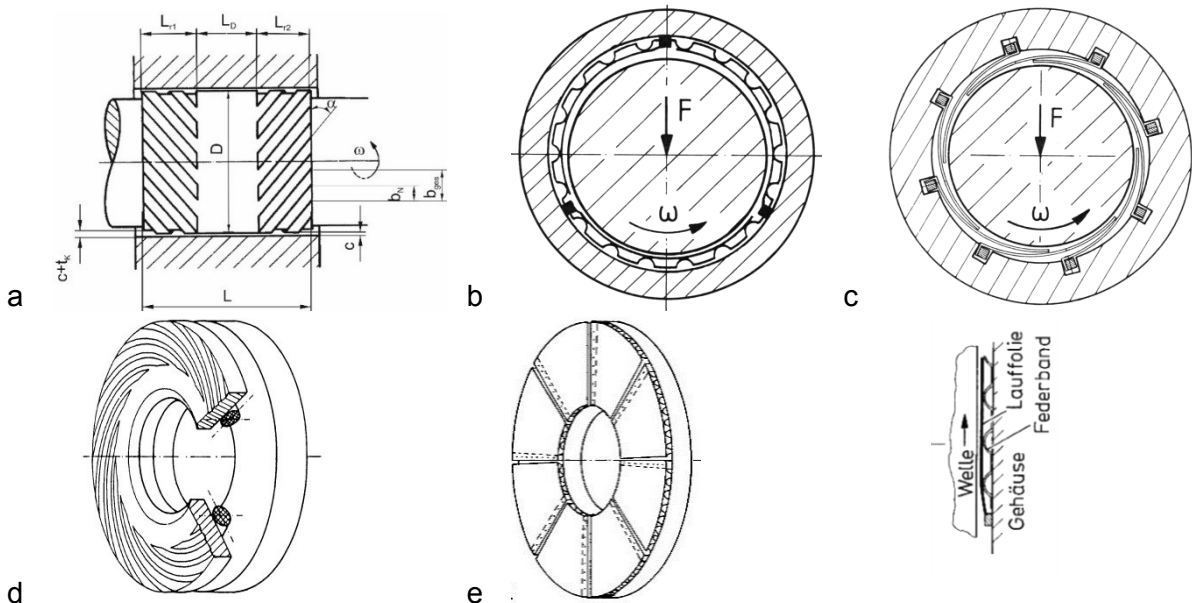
Lagerbauformen: a) Herringbone Bearing, b) Bump-type Bearing, c) Leaf-type Bearing, d) Spiral-grooved Thrust Bearing, e) Bump-Foil Thrust Bearing
